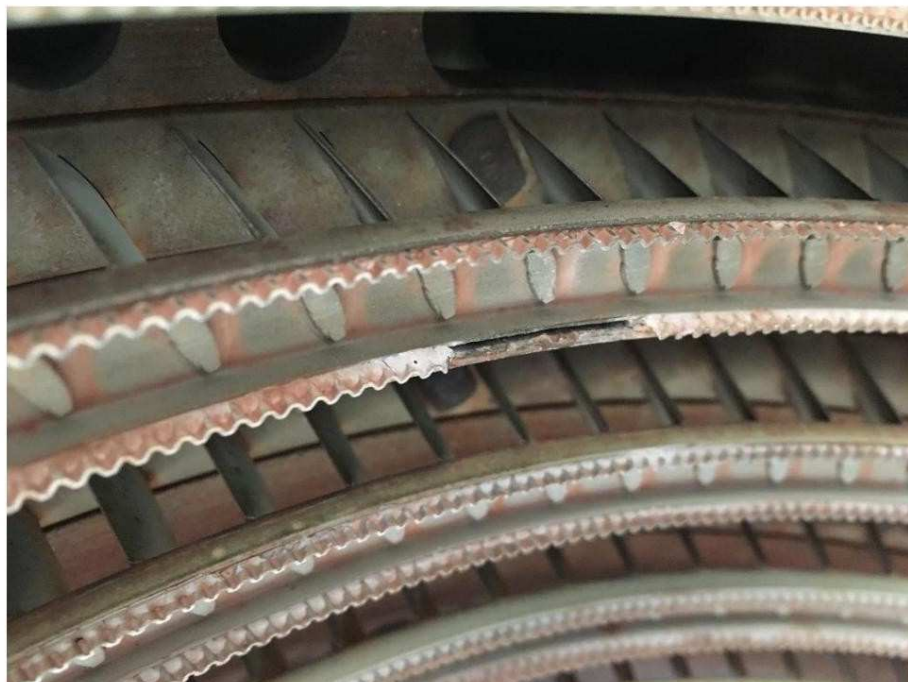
Section manquante de la bande d'étanchéité à l'air
